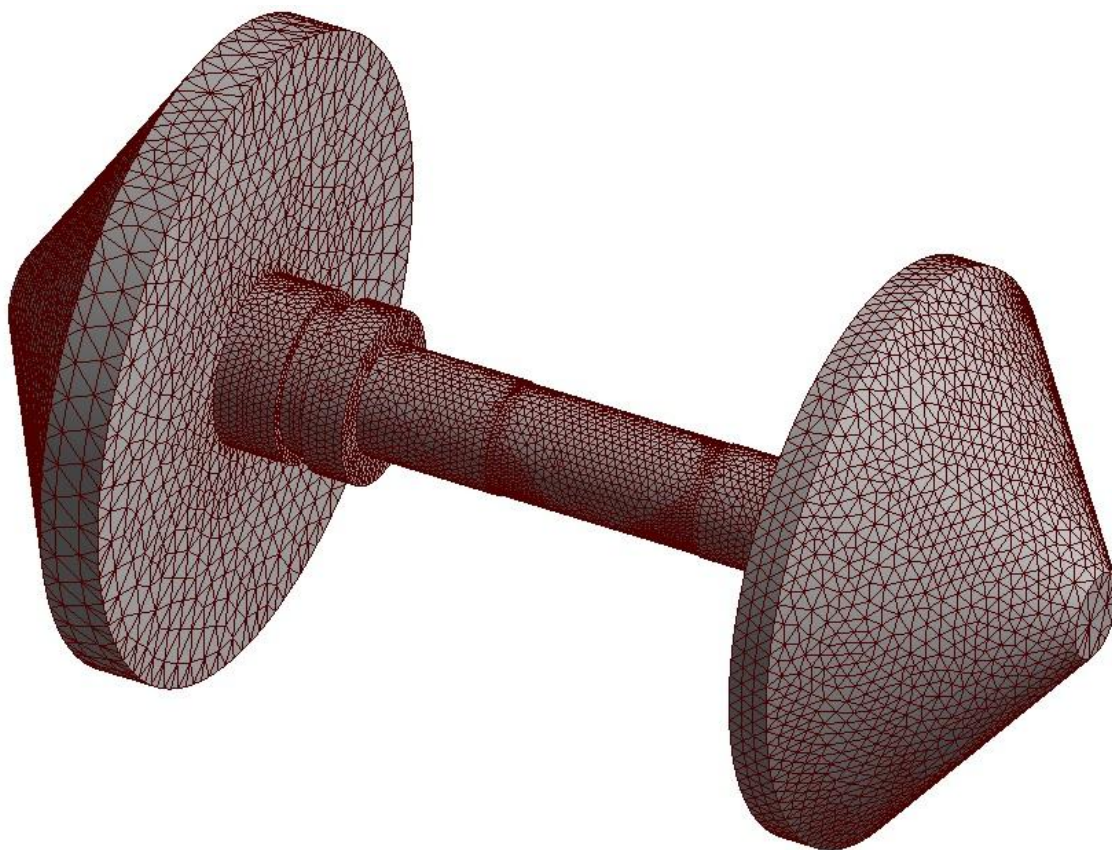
Zjednodušený model rotoru (AutoCAD Inventor)
